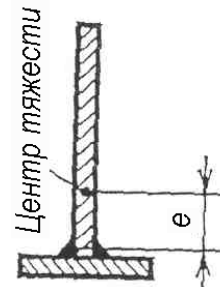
Продольная деформация сварной балки и схема ее нагружения
